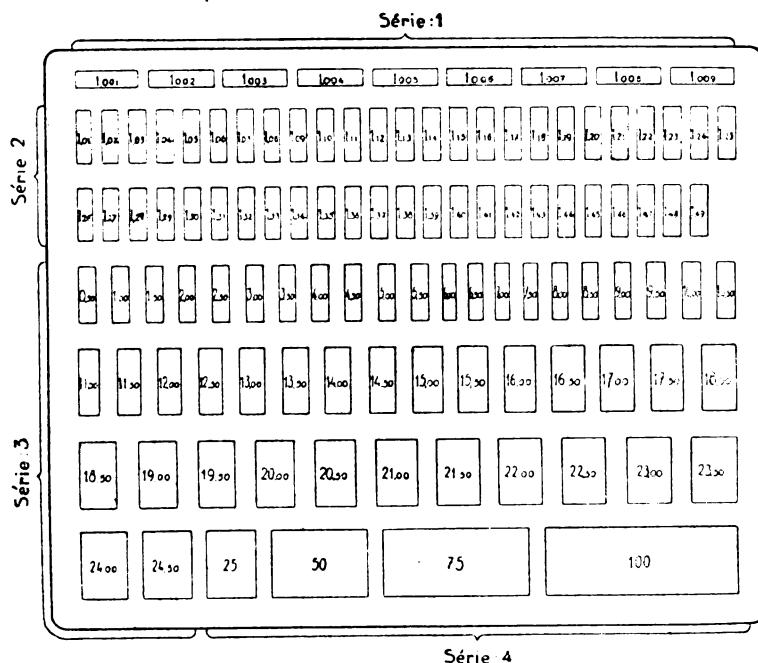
Jeu de calibres par millièmes de millimètre.
